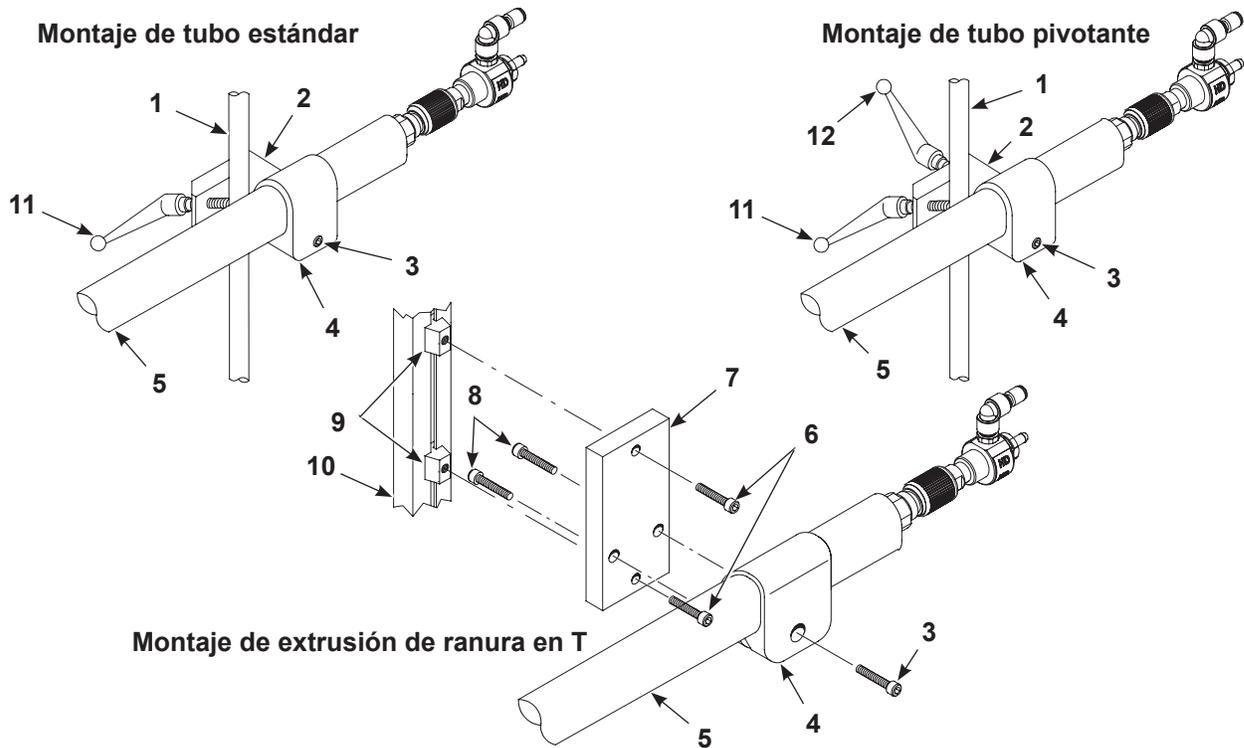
Conjuntos de montaje de la pistola de aplicación de montaje en tubo
